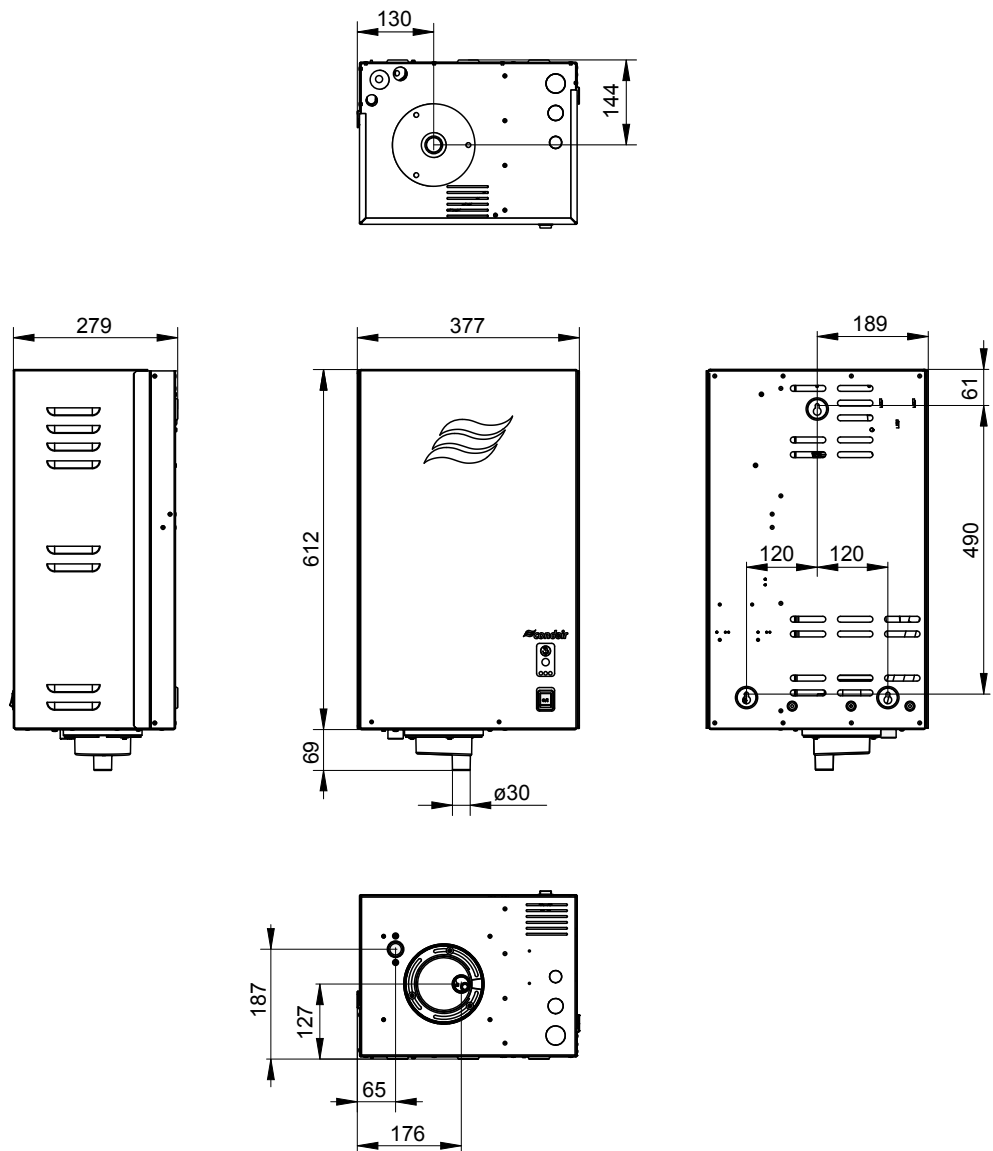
Geräteabmessungen Condair Sigma 5-15
